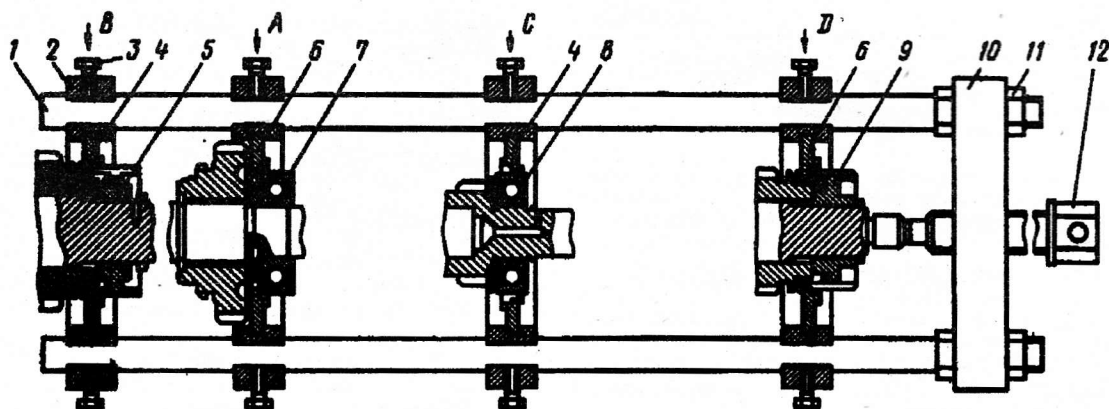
Съемник 7823-6088-01 для снятия подшипников и ступиц с первичного и вторичного валов:
